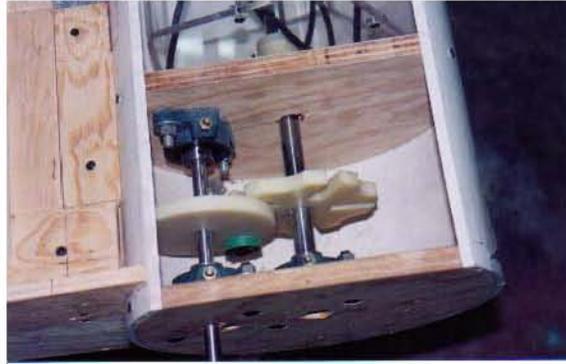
(b) Montaje del mecanismo “freno de Ginebra” en el equipo
